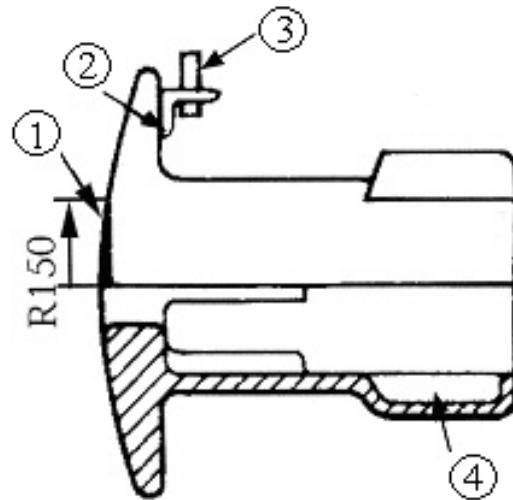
Дефекты буферного стержня, ремонтируемые сваркой или наплавкой
